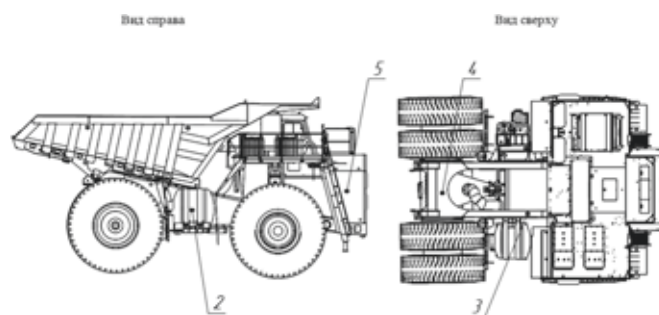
Компоновочная схема установки криогенного топливного бака на правом лонжероне рамы карьерного самосвала «БелАЗ-75306»: 2 – криогенный топливный бак; 3 – правый лонжерон; 4 – рама; 5 – карьерный самосвал «БелАЗ-75306» /
